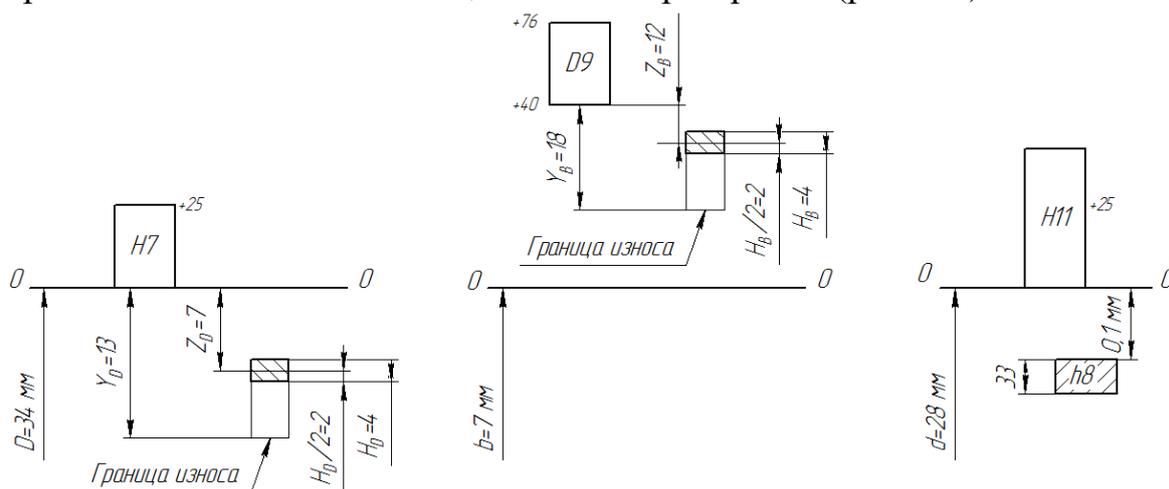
Схема полей допусков комплексного шлицевого калибра-пробки
